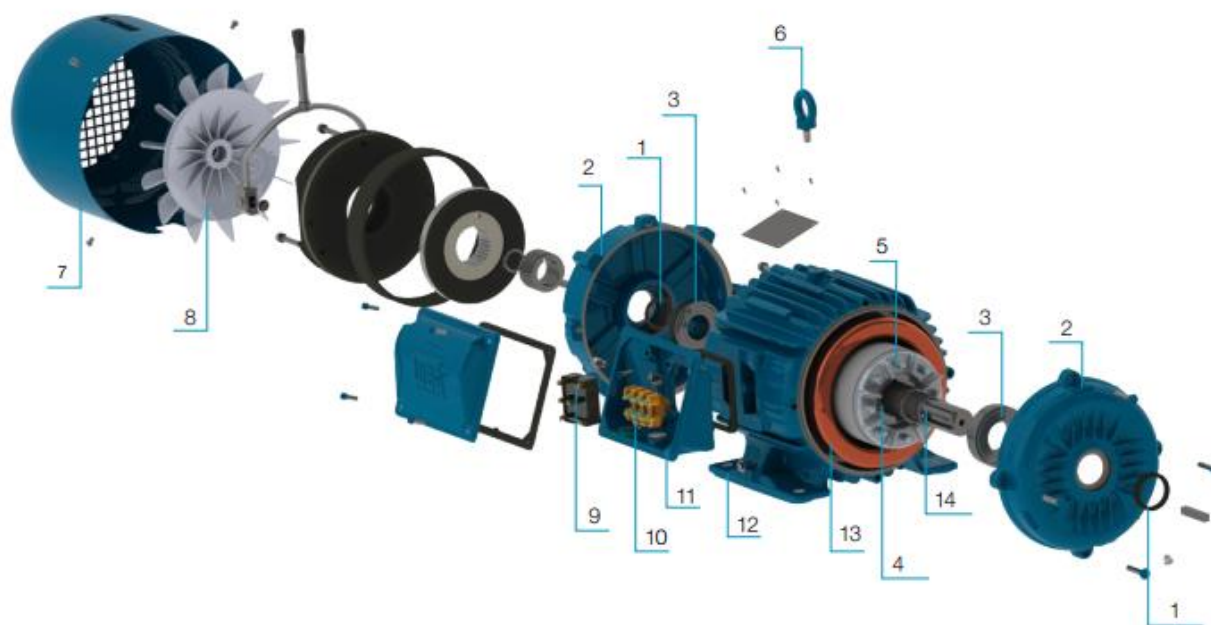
Principais componentes do motor de um Motofreio WEG W22 (Fonte:WEG)
